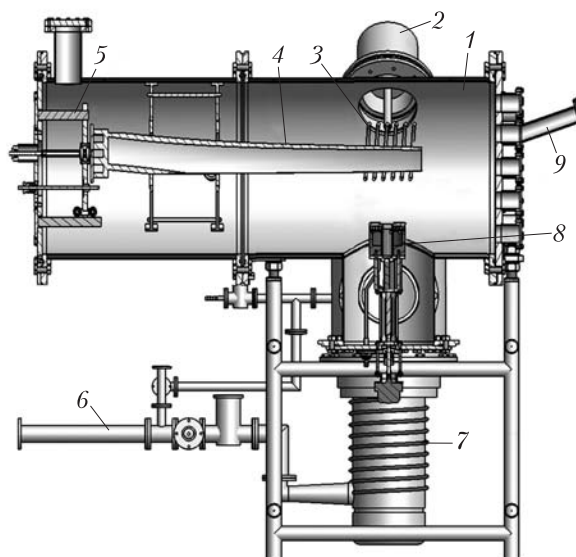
Схематическое изображение продольного сечения вакуумной камеры установки: 1 – вакуумный объем; 2 – электронно-лучевая пушка; 3 – индуктор; 4 – упрочняющая деталь (лопатка паровой турбины); 5 – механизм крепления и подачи образца; 6 – вакуумная откачка; 7 – вакуумный насос; 8 – тигель; 9 – окно видеонаблюдения
